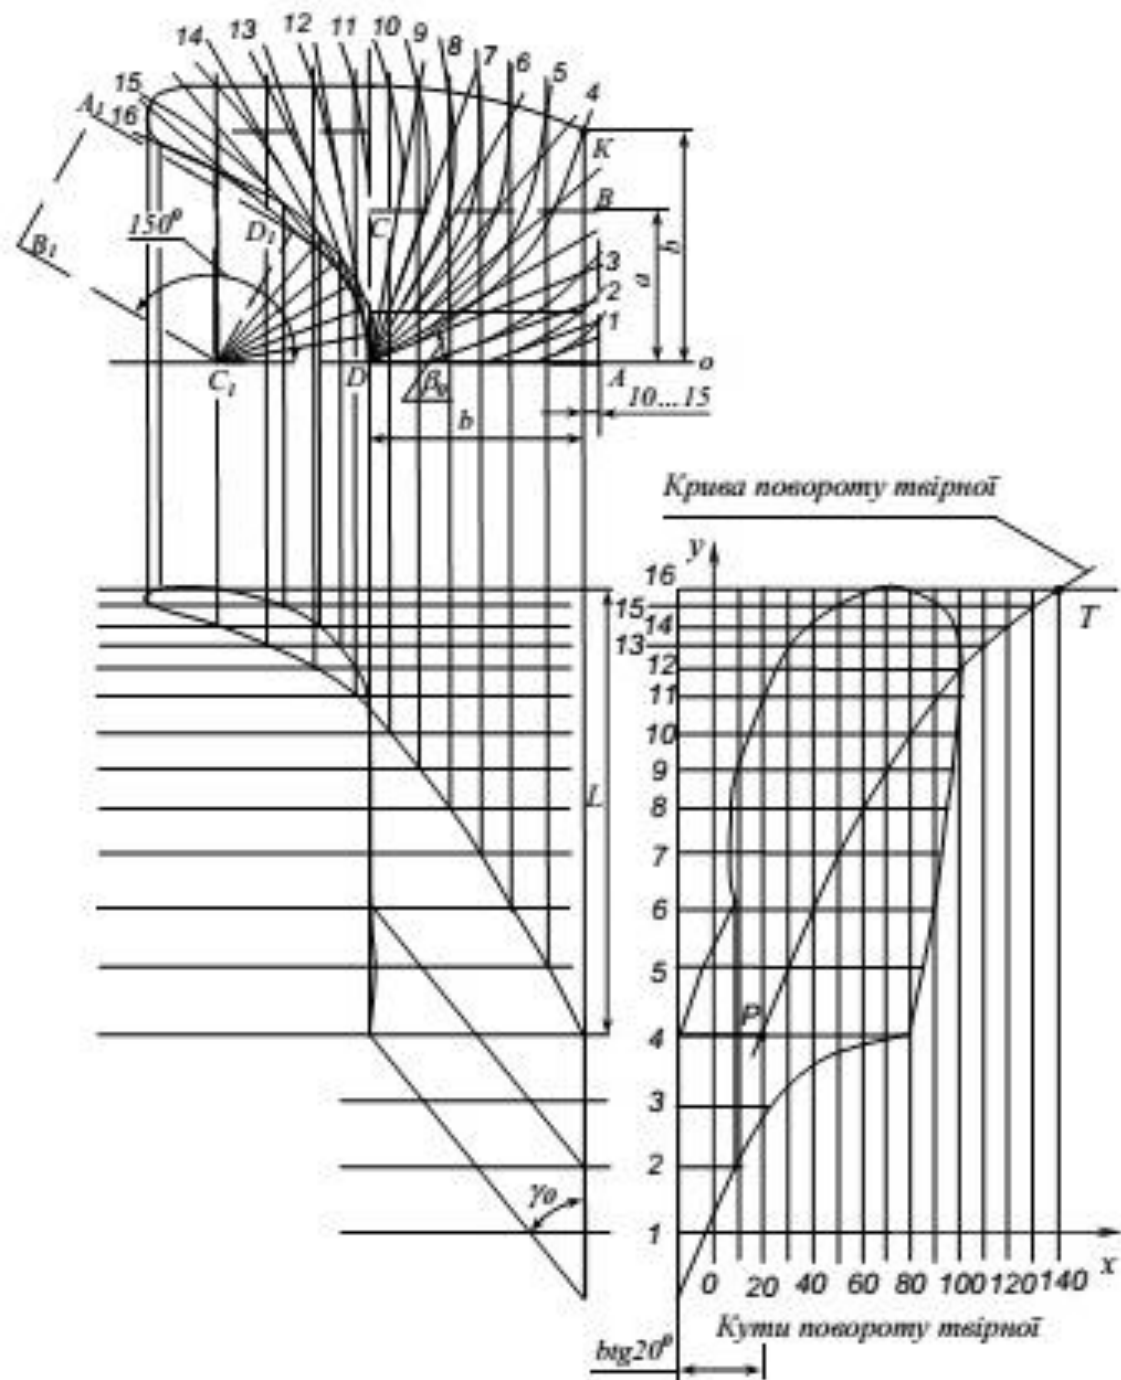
Побудова гвинтової робочої поверхні
